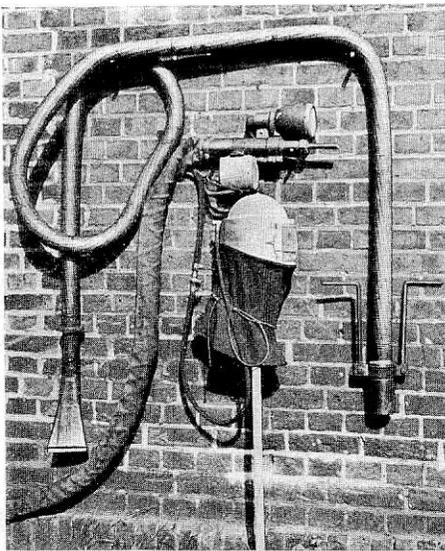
Saugrüssel zum Entfernen des Gebläsesandes.
